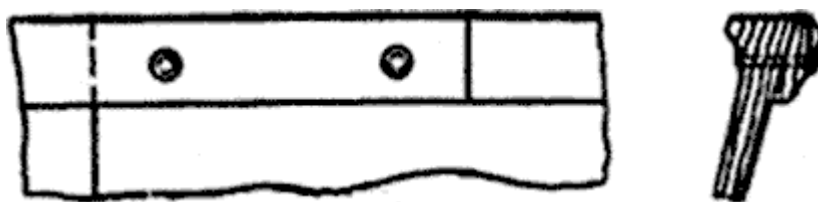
Стык двух половин верхней обшивочной доски и его крепление.
